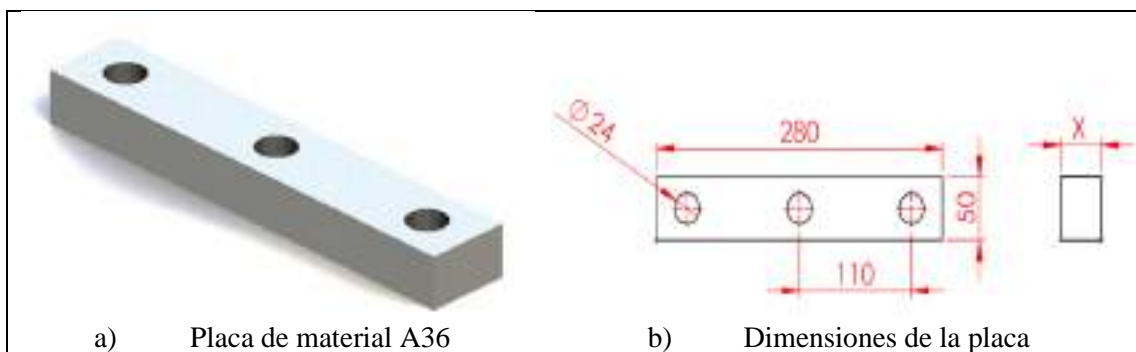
Diseño de la placa superior de la base de los rodamientos
